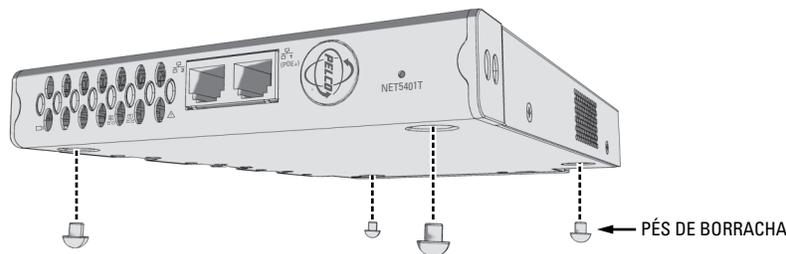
Fixação dos pés de borracha para posicionamento sobre a mesa
